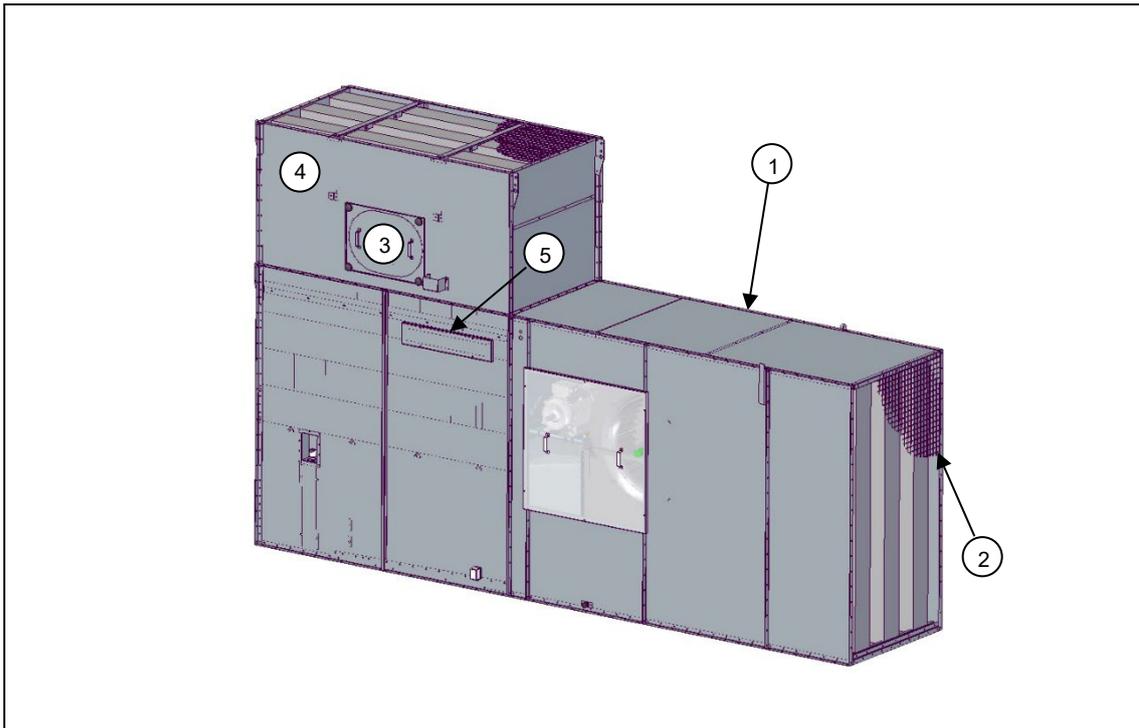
Kühlturm mit Schalldämpfer – seitlich ansaugend – oben ausblasend
